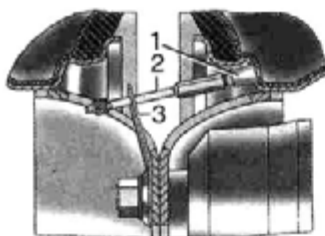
Установка удлинителя вентиля шин задних колес:
